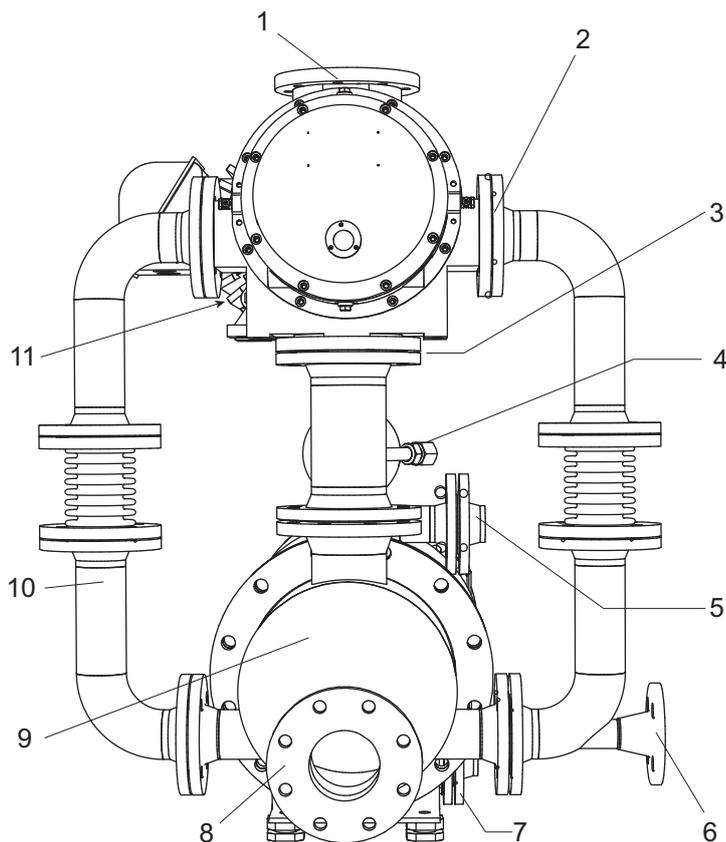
Wälzkolbenpumpe mit Röhrengaskühler
